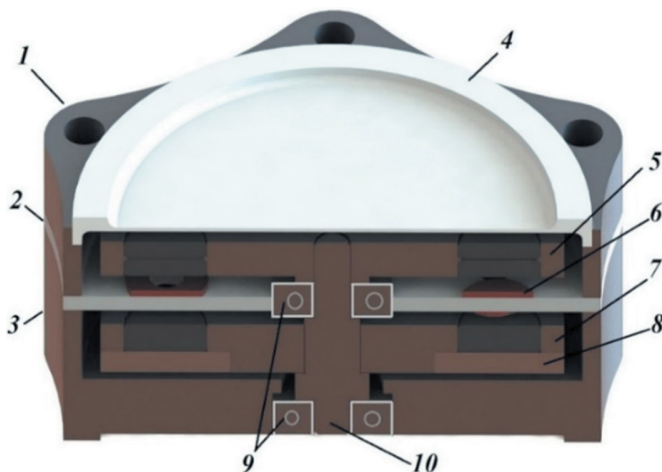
Проектируемая конструкция привода: 1 – верхний корпус привода; 2 – пластина статора; 3 – нижний корпус привода; 4 – крышка; 5 – верхний ротор; 6 – управляющая обмотка; 7 – нижний ротор; 8 – замыкающее кольцо; 9 – подшипники; 10 – вал
